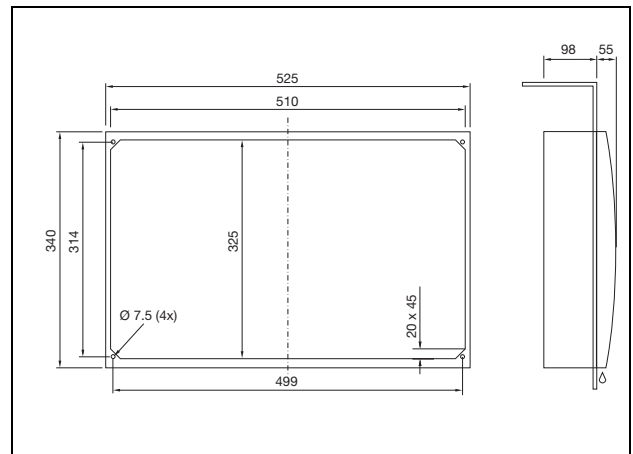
3328.xxx, 3329.xxx částečně zapuštěná montáž
